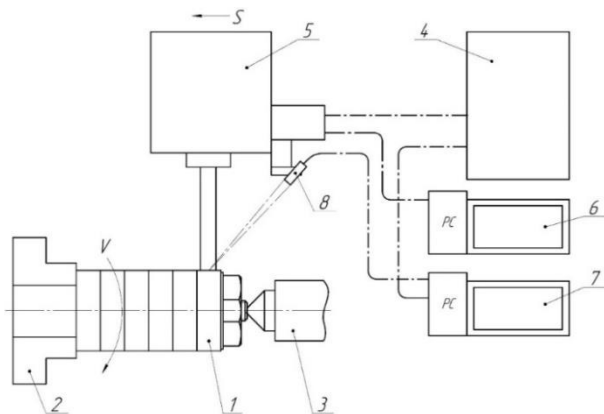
Схема лазерной заковки: 1 – заготовка; 2 – патрон; 3 – задний центр; 4 – источник лазерного излучения; 5 – оптическая головка; 6 – контроллер ЧПУ; 7 – контроллер температуры; 8 – пирометр
